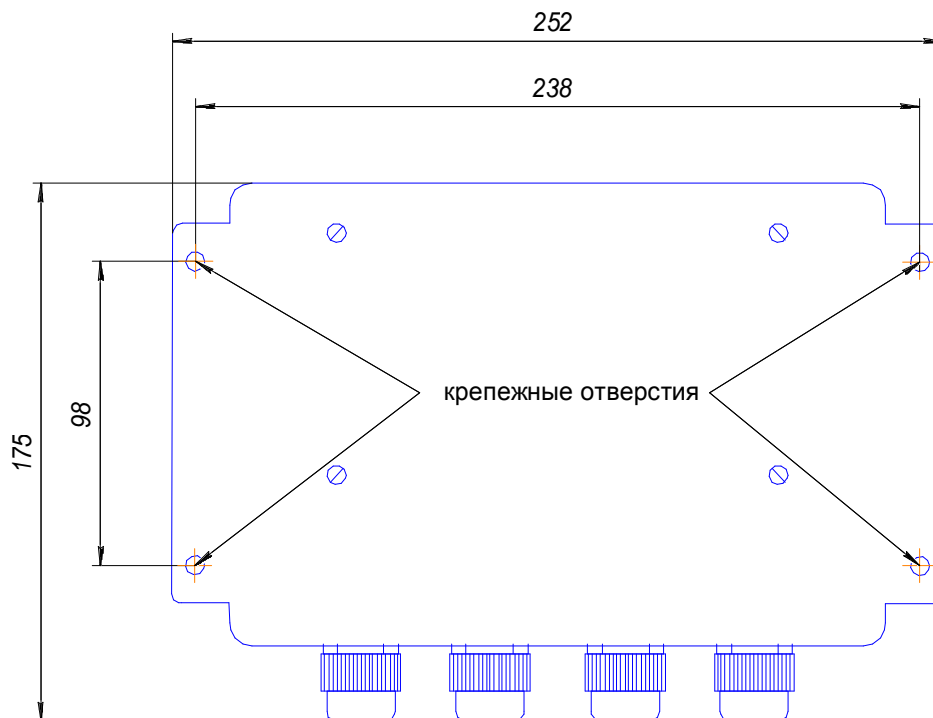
г. Разметка крепления на стену АКШ-801 ФИДШ.426461.001-03 в металлическом корпусе для эксплуатации на улице.
